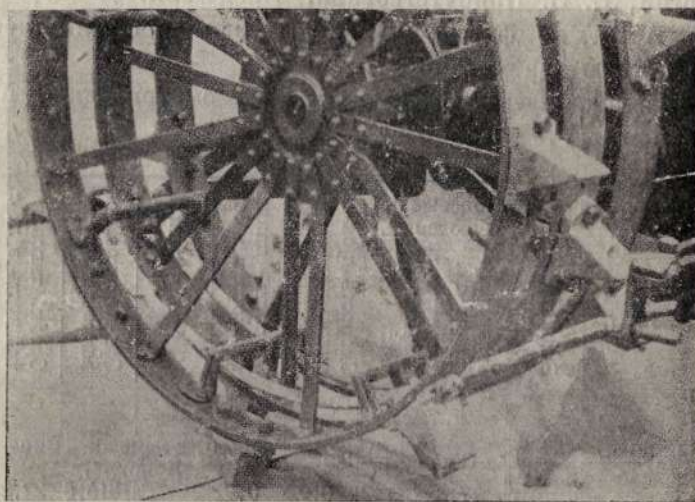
Приспособление для очистки обода трактора «Виккерс».
